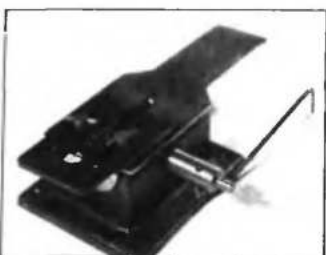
Приспособление с алмазным кругом для ручной подгонки замков поршневых колец
